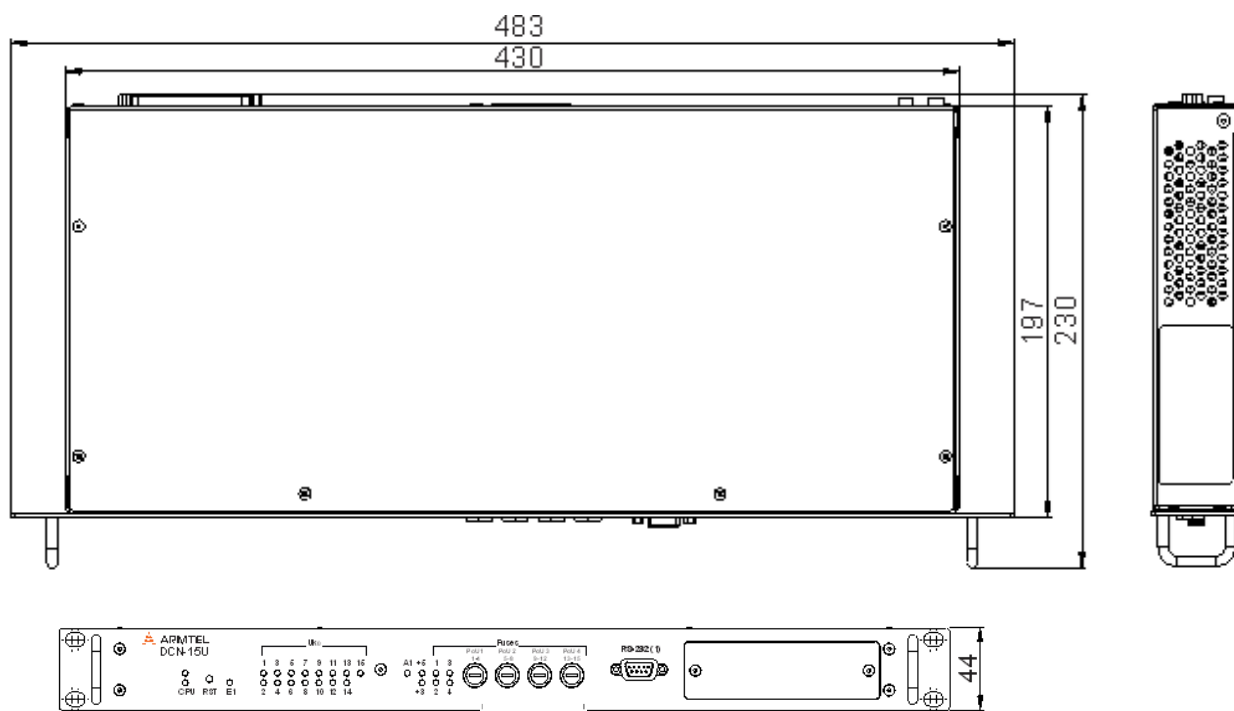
Внешний вид и габаритные размеры DCN-15U основного исполнения
